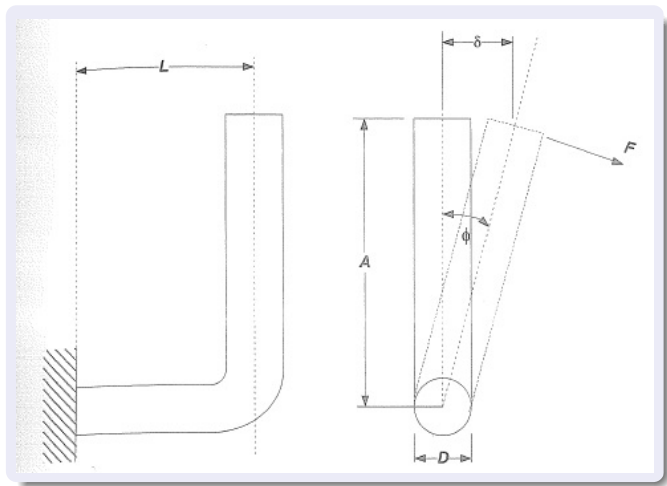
Planilha para cálculo da barra anti-rolagem.
